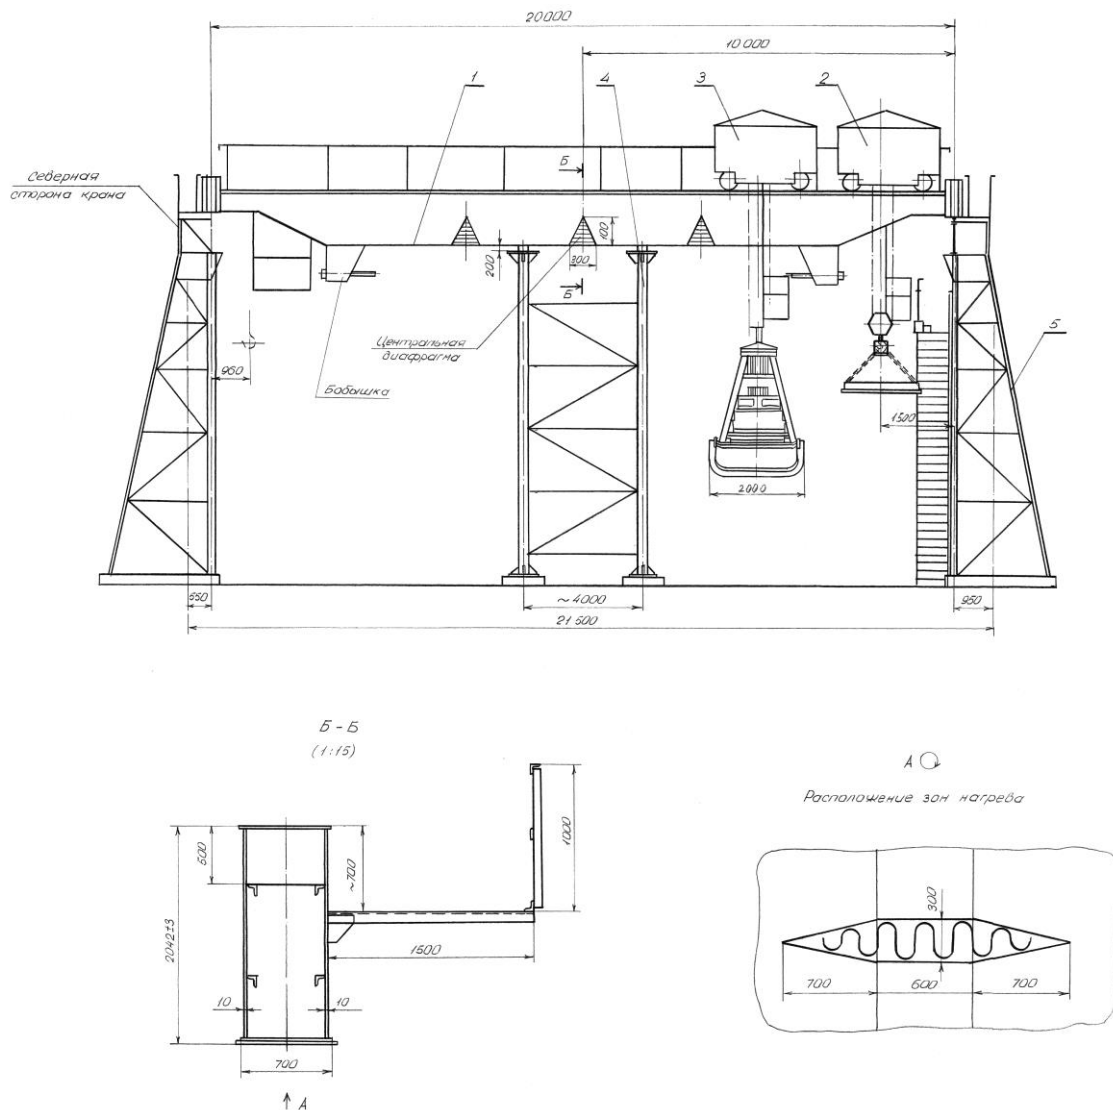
Монтажна схема щодо ремонту головної балки моста: 1 – головна балка; 2 – візок магнітний; 3 – візок грейферний; 4 – портал; 5 – сходи
